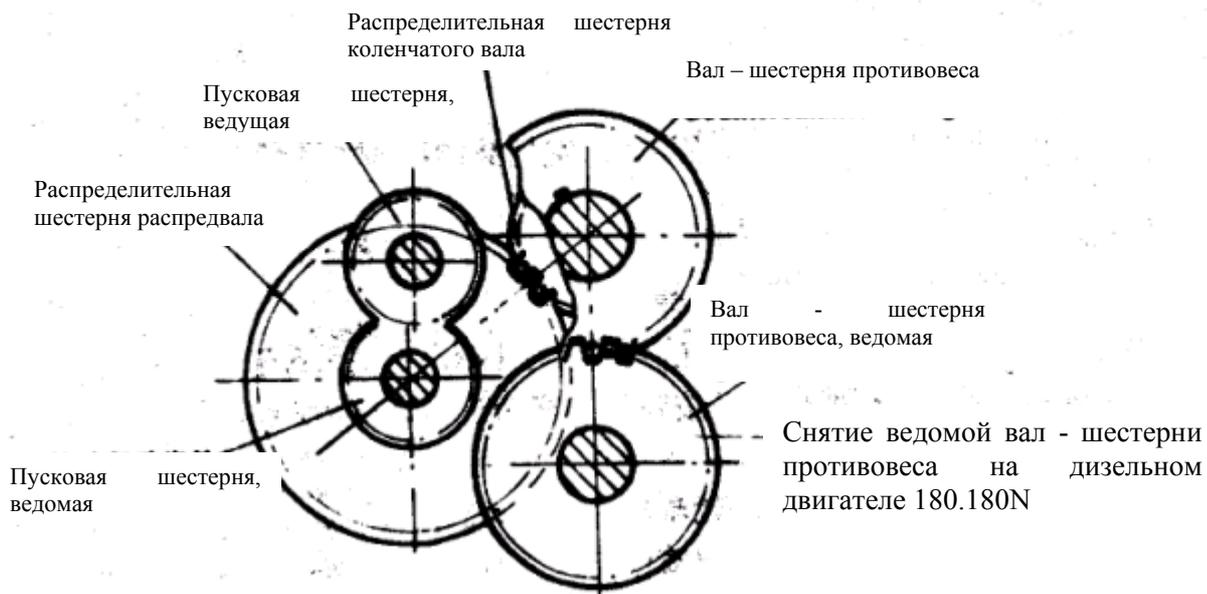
Точки зацепления шестерен на дизельном двигателе 185
